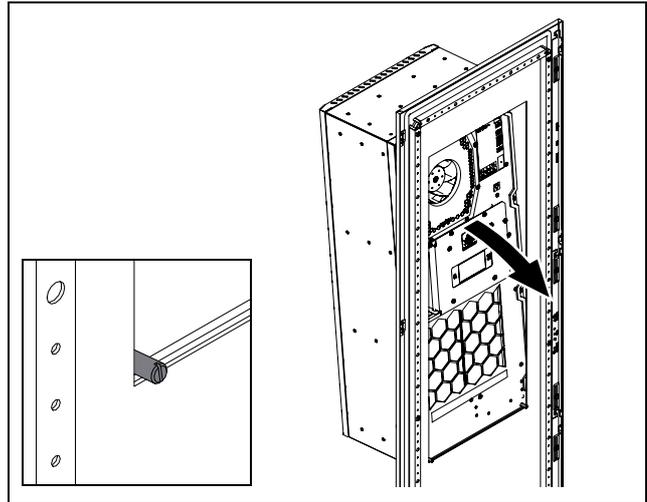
Colocación del refrigerador en la escotadura de montaje
